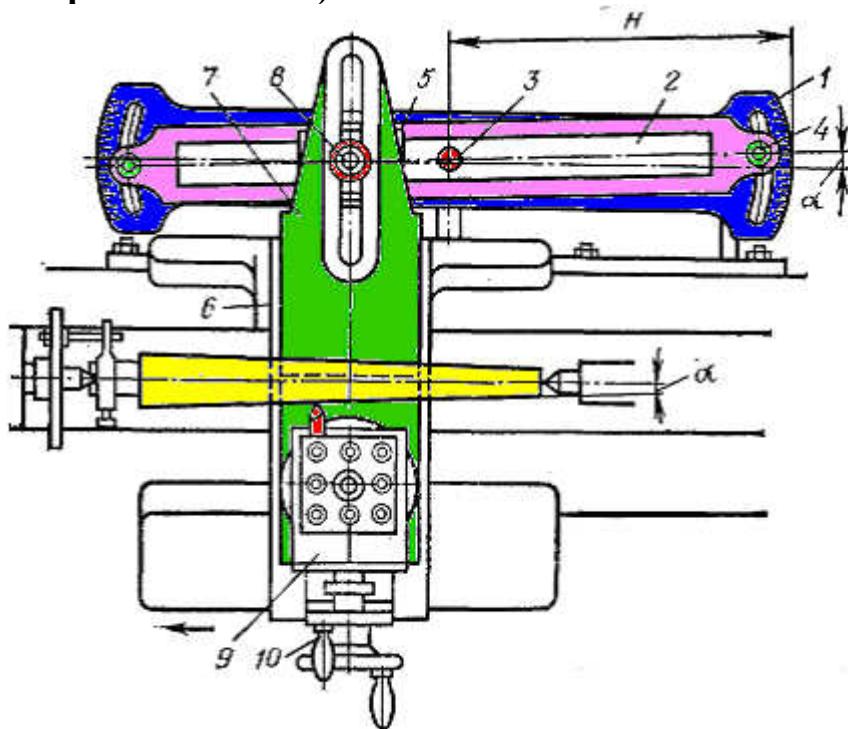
Схема точения конической поверхности с помощью конусной линейки:
